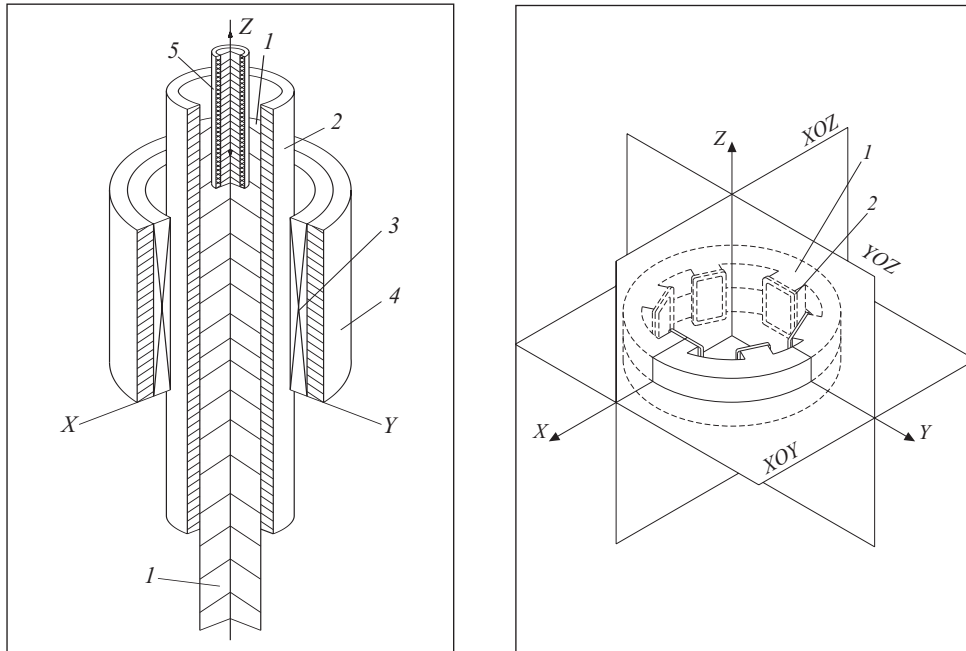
Схема конструкции системы кристаллизатор МНЛЗ—ЭМП: 1 — заготовка круглого сечения; 2 — кристаллизатор; 3 — трехфазная обмотка ЭМП; 4 — магнитопровод; 5 — погружной сталеразливочный стакан
